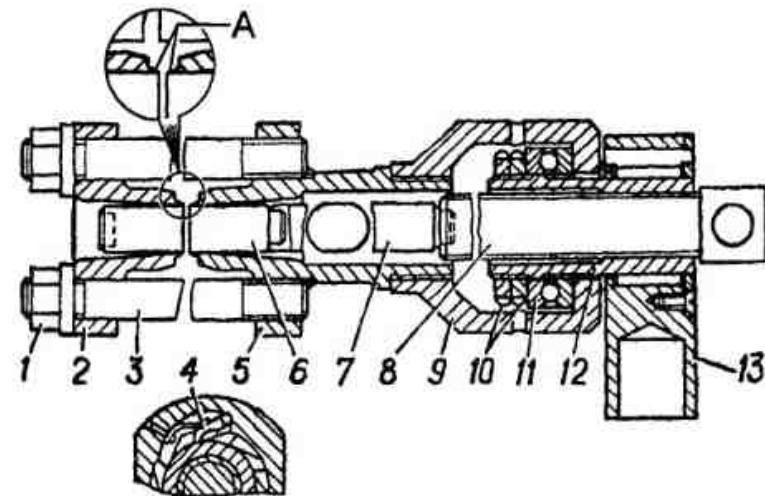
Приспособление для выпрессовки и запрессовки пальцев с РМШ:
